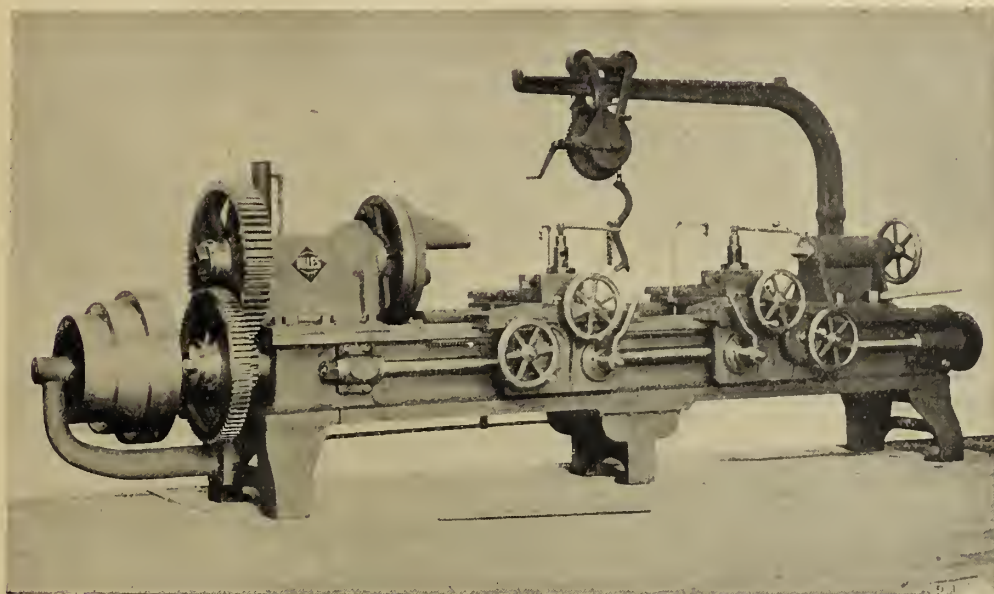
Tour double des *Niles Tool Works*, pour locomotives.
